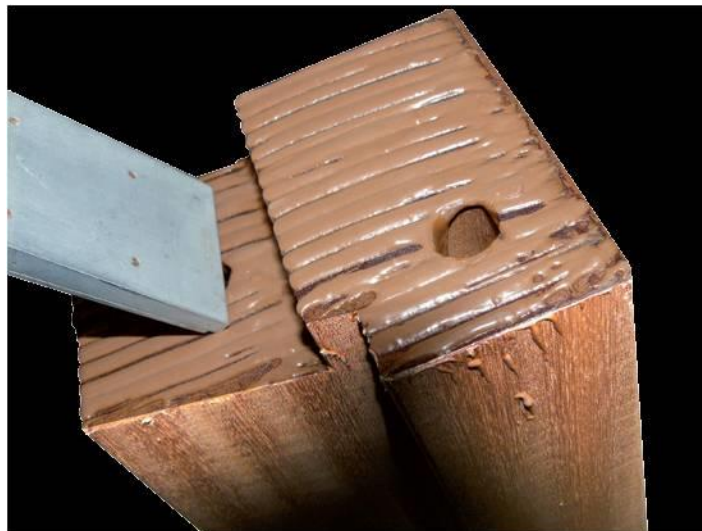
Verdeling van DRYWOOD Opti-Joint XP met doseerspatel
